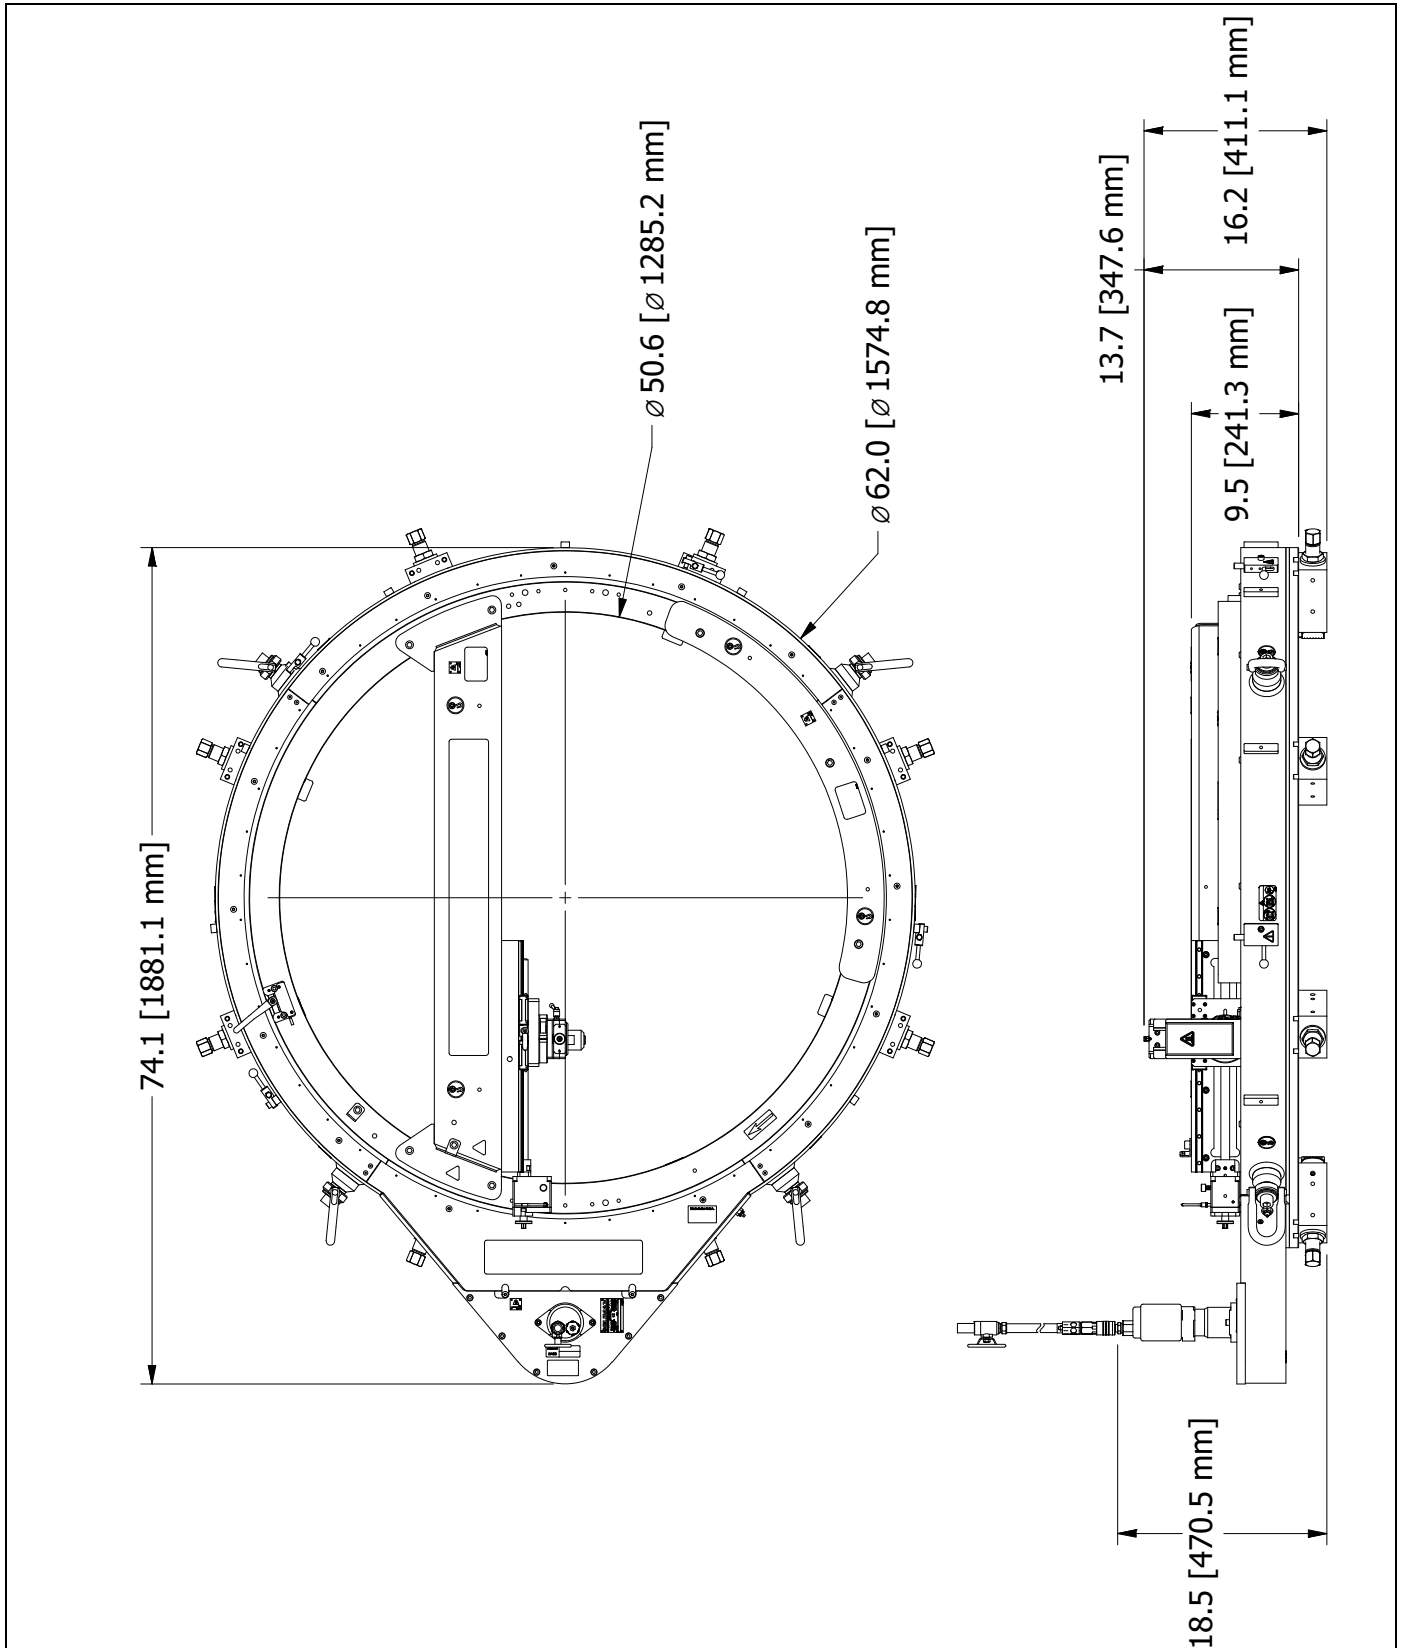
DIMENSIONES DE ODF50 SPEED FACER (N/P 86980)
